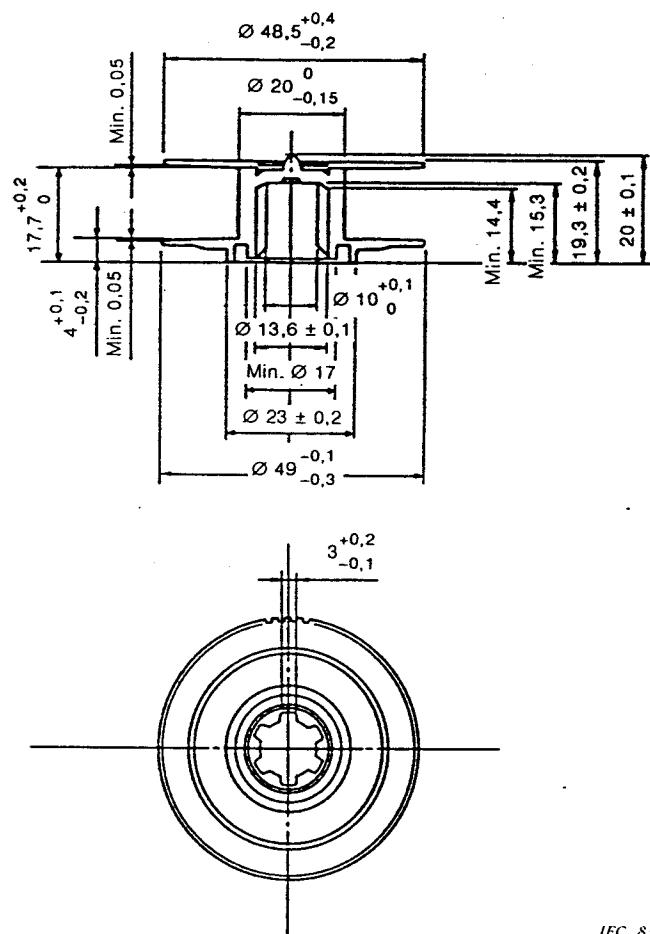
Dimensions de la bobine réceptrice de la cassette de petite dimension
